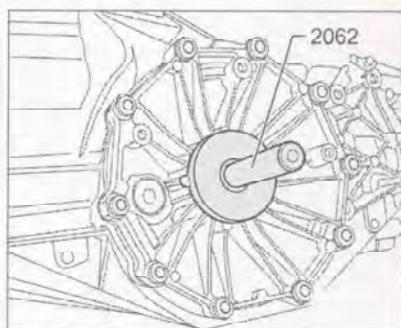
С помощью приспособления 2062 установите новый сальник левого вала на глубину 5.5 мм в крышку главной передачи.
